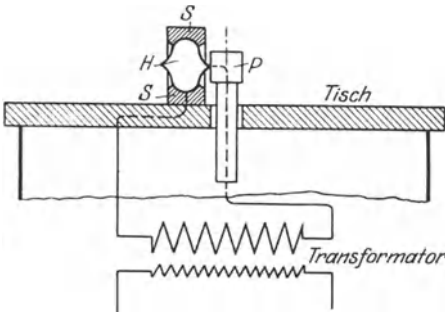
Schema der Hohlkörperschweißung.
